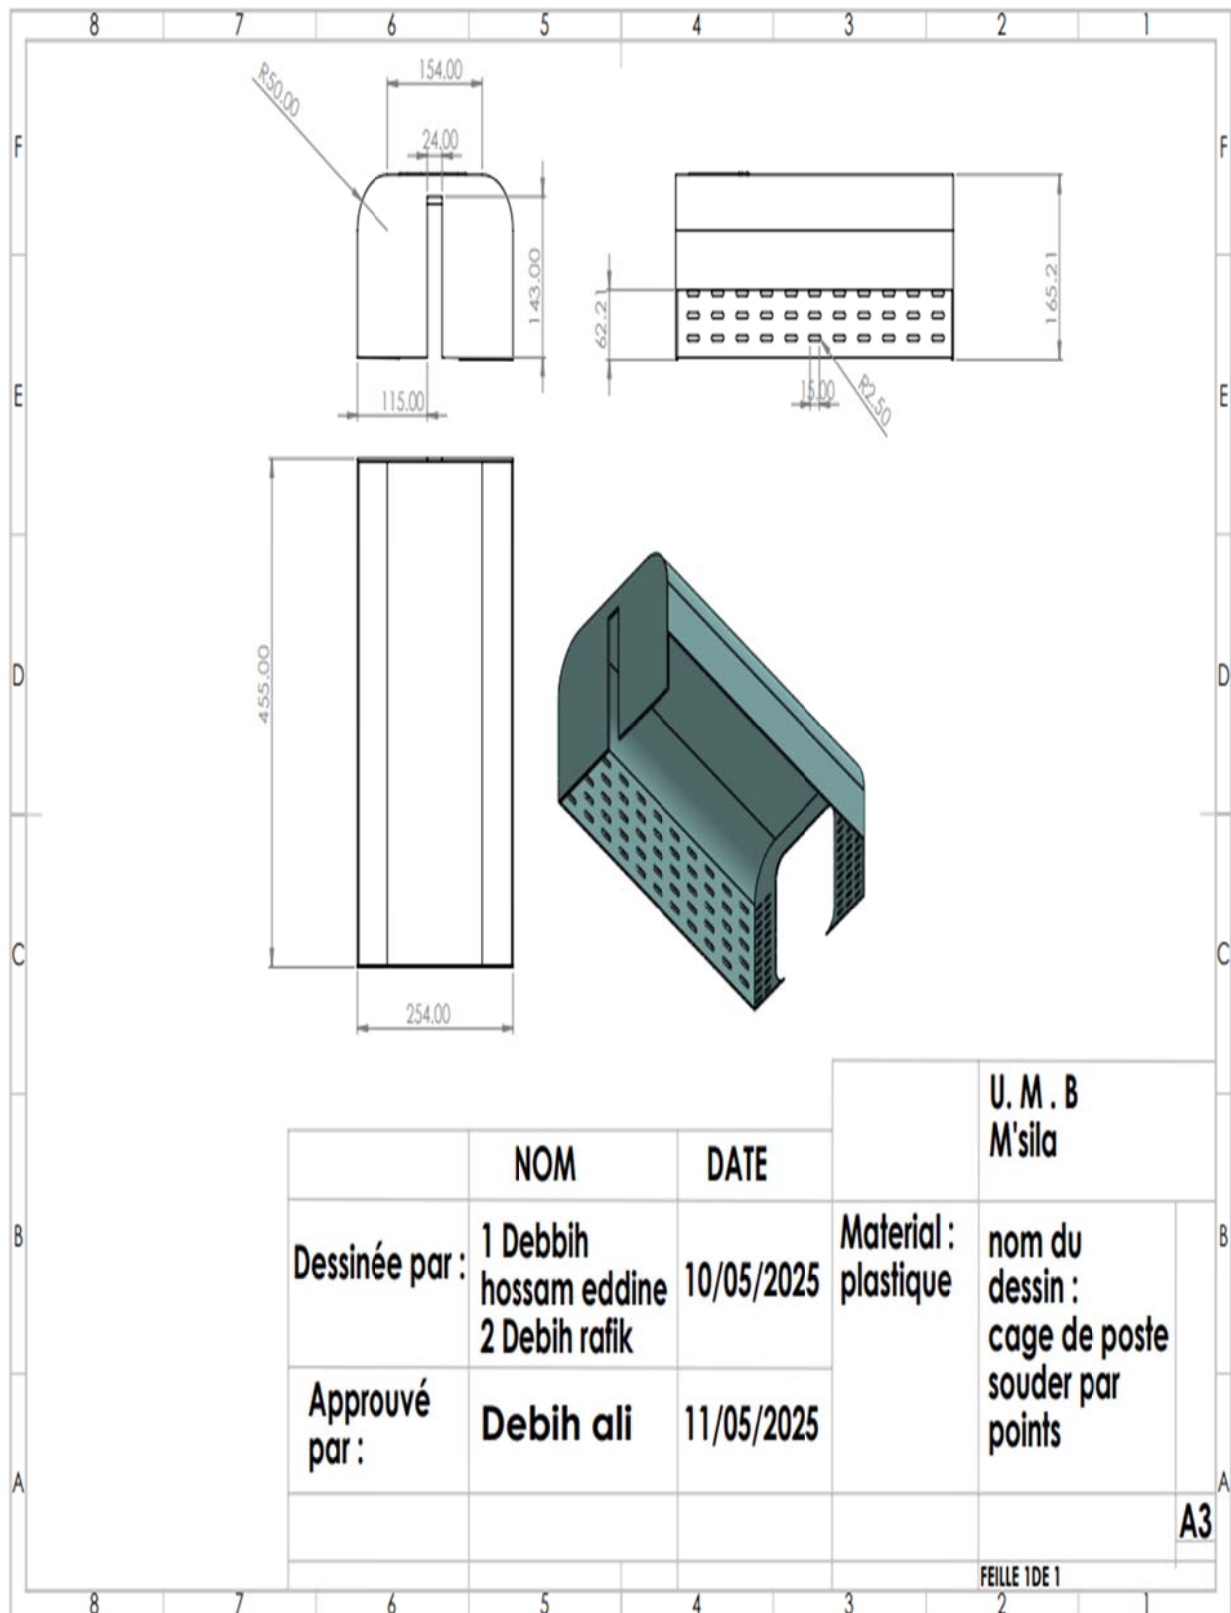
Découpe et assemblage des pièces de la Couverture.
